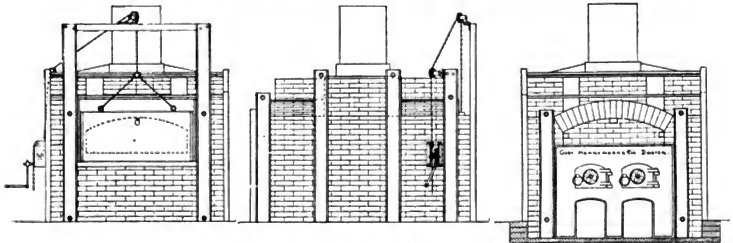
Ofen zum Oberflächenhärten von Geldschrankplatten.
